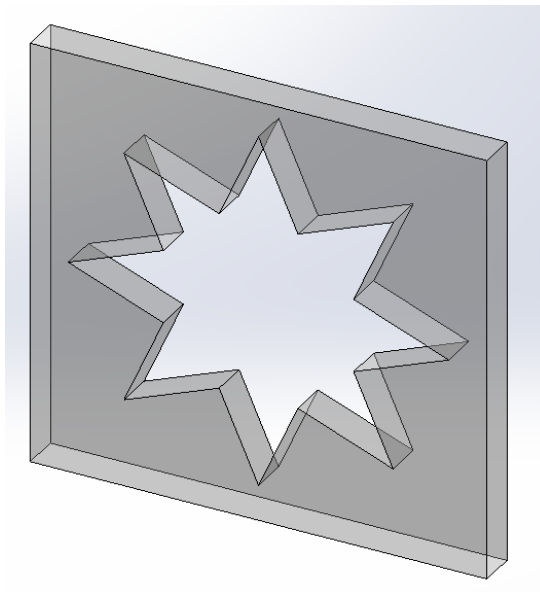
Solido 1 Corte avanzado. Fuente: Creación propia
